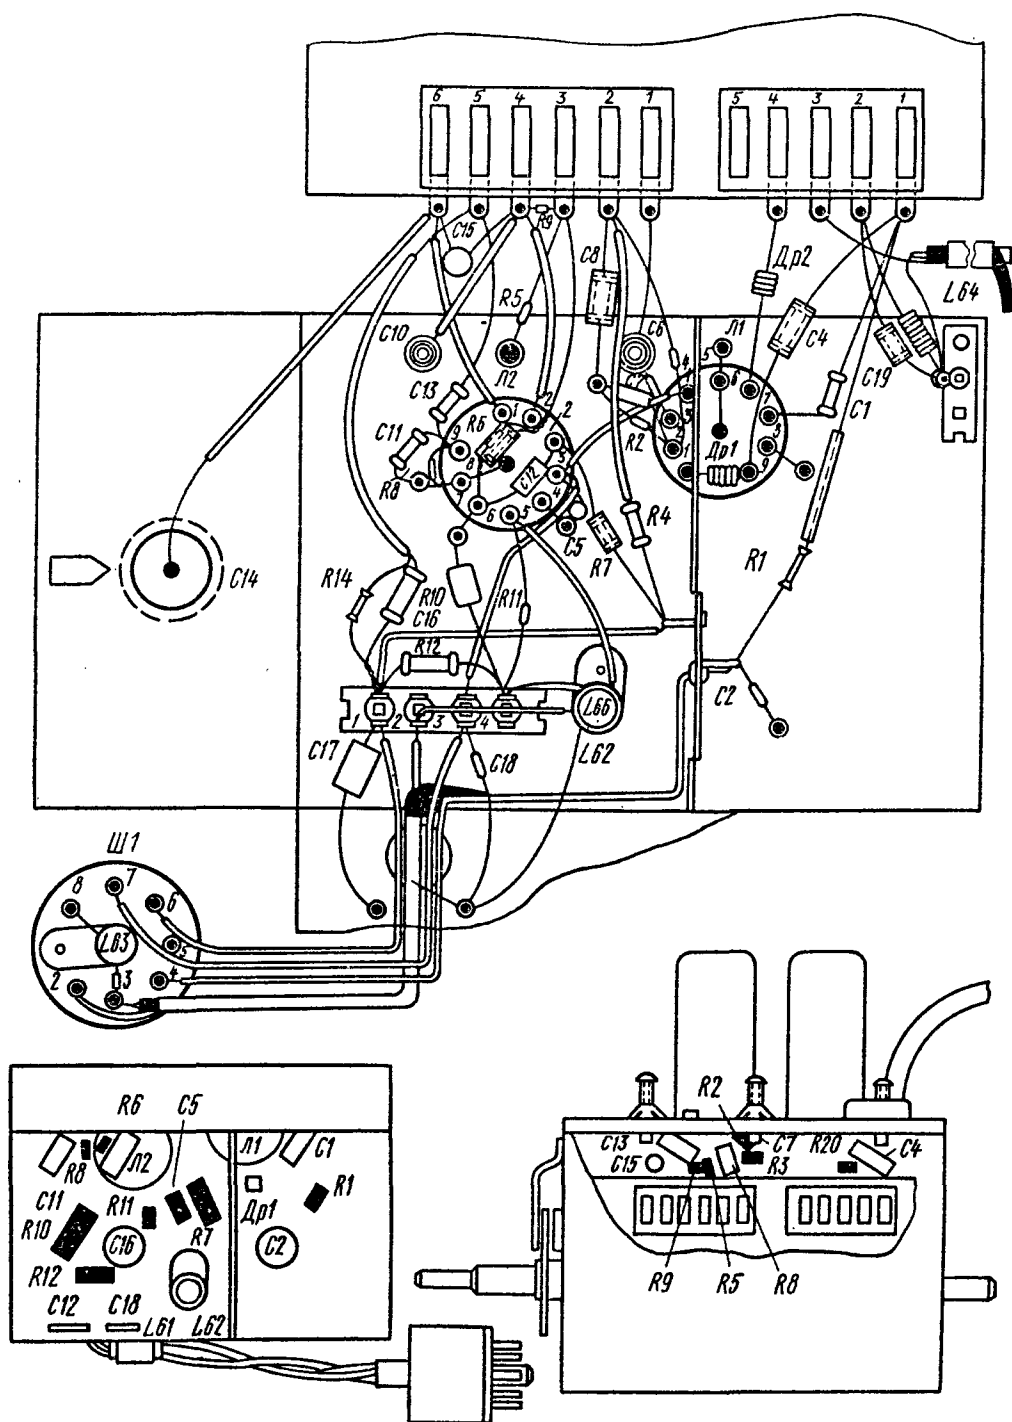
Монтажная схема и расположения деталей в ПТК
